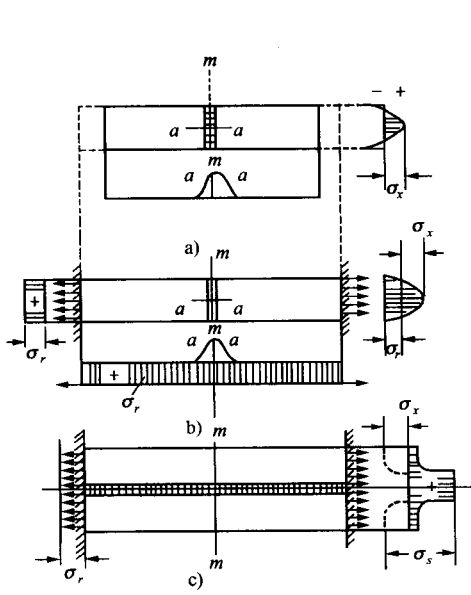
在对接焊缝上的焊接残余应力和拘束应力
